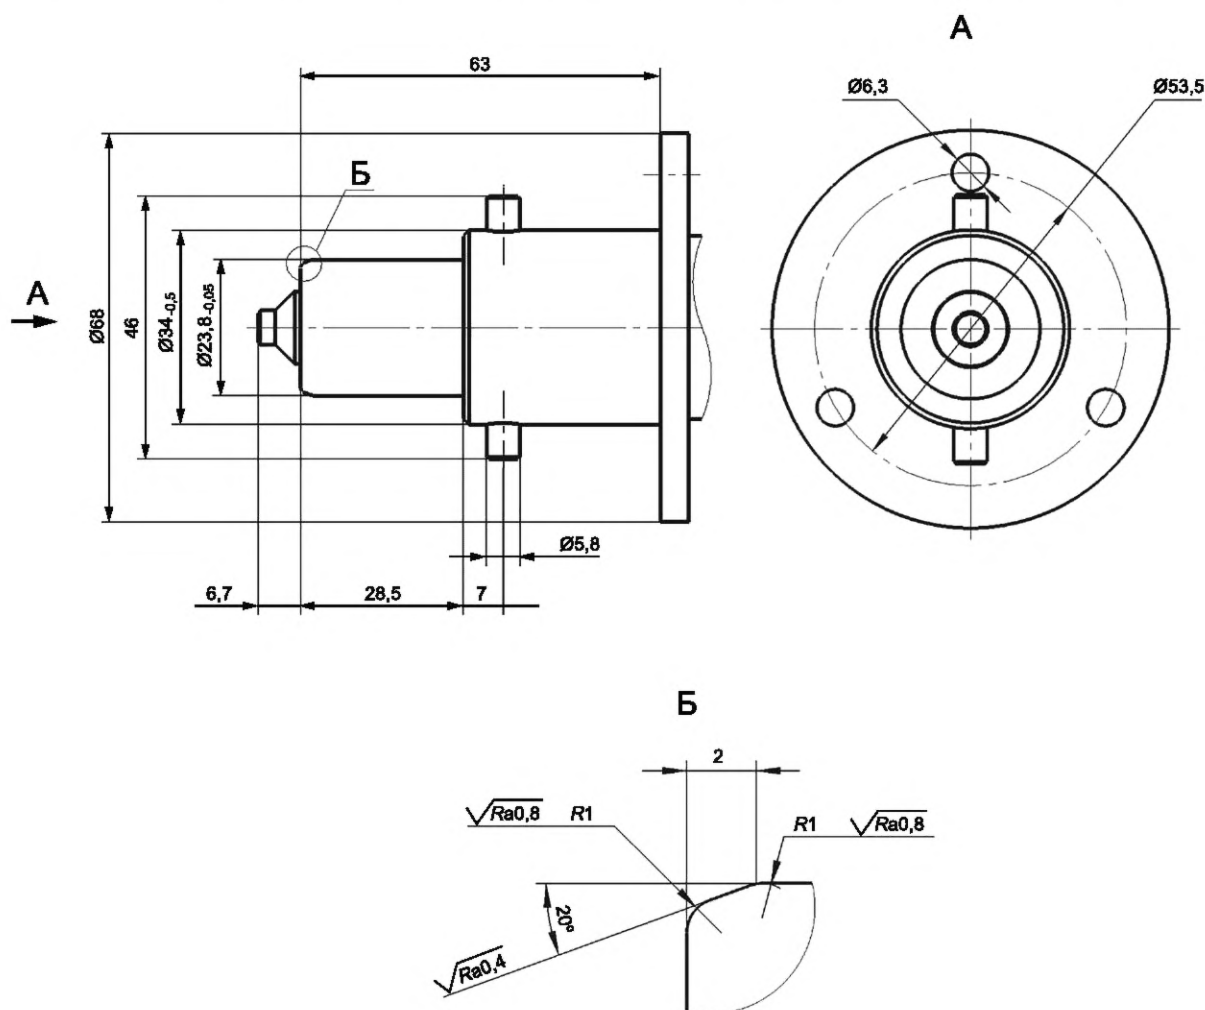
Размеры адаптера быстроразъемного соединения отпарного газа
